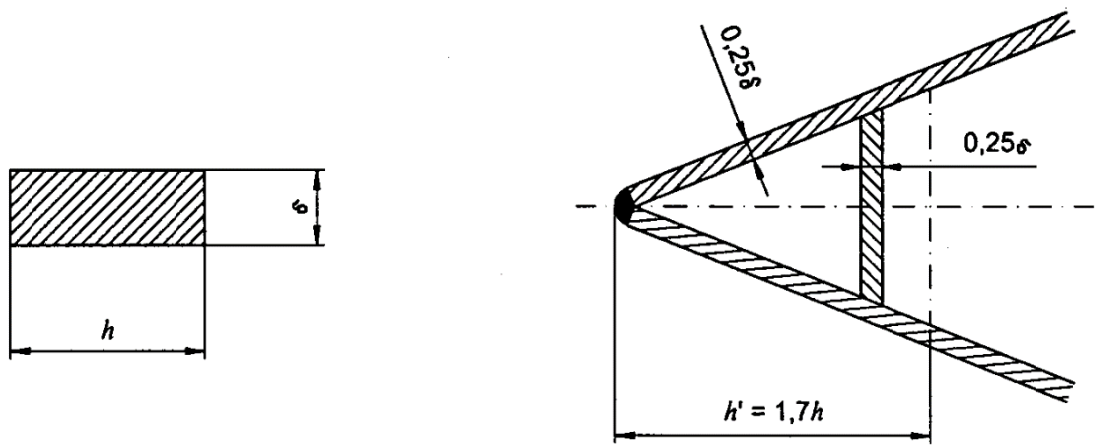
Брусковий і зварний форштевень
